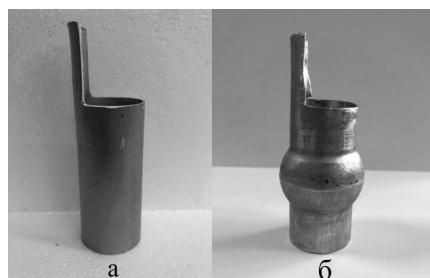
Испытательные образцы из алюминиевого сплава Д16
